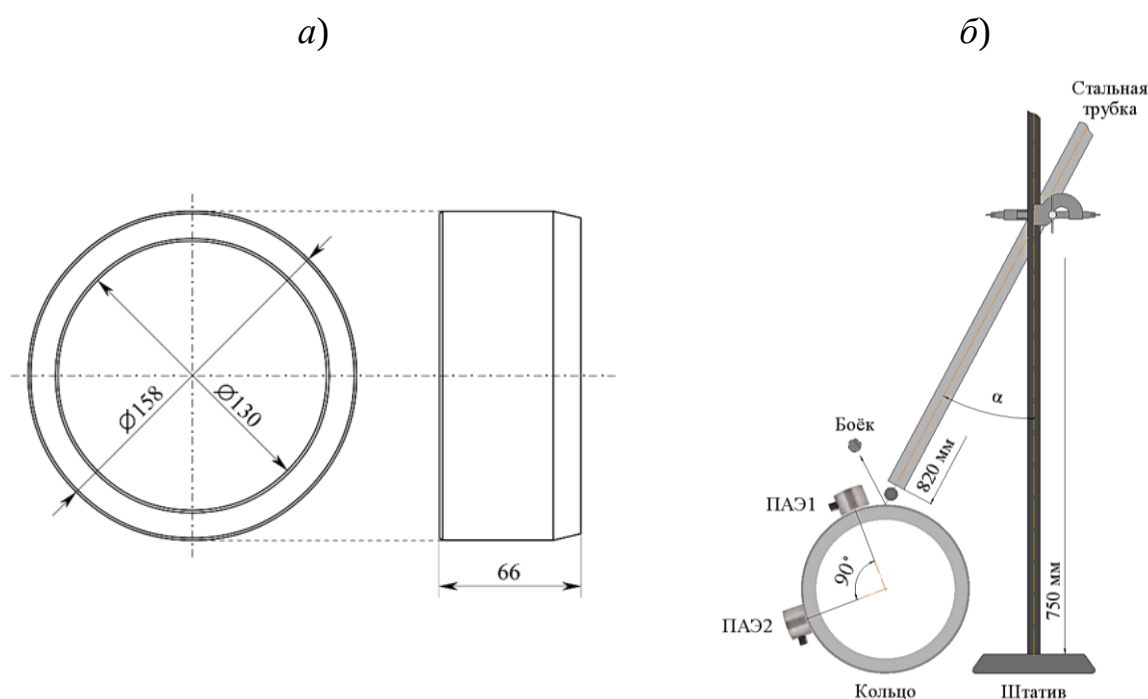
Схематическое изображение безбуртового кольца подшипника (а) и схема расположения преобразователей 1 и 2 и способа удара (б)
